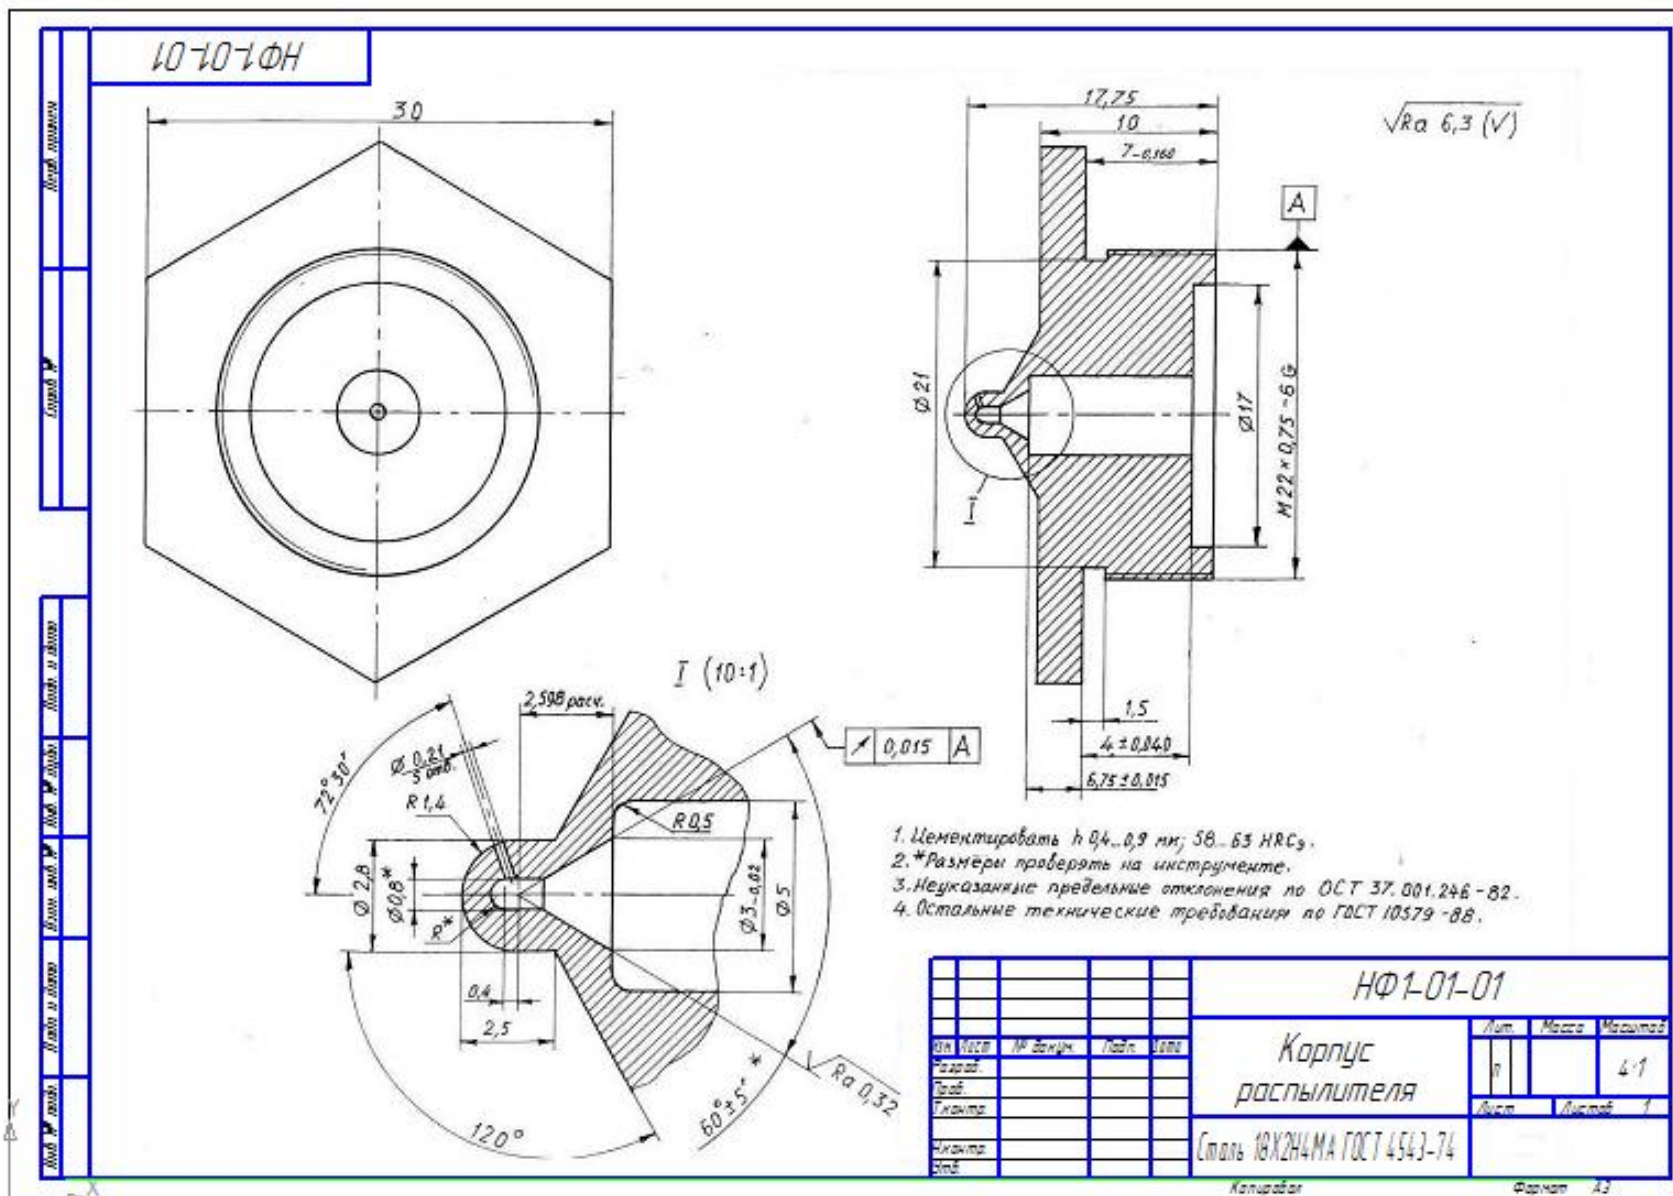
Пример выполнения рабочего чертежа детали «Корпус распылителя»
